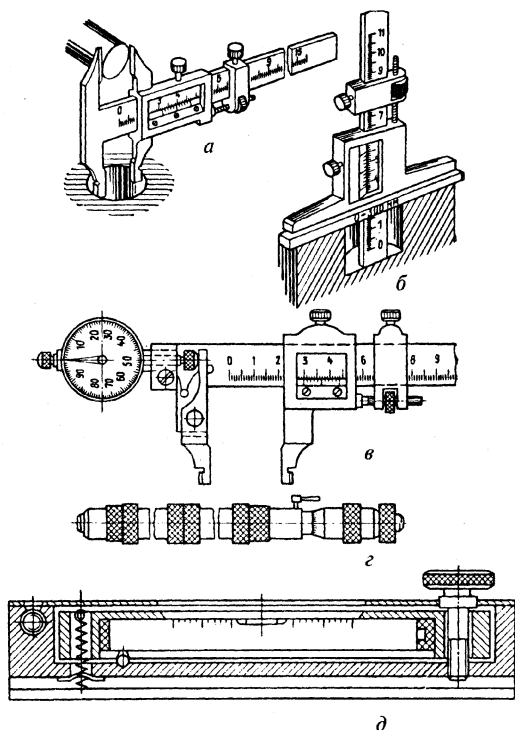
Инструменты для контроля точности сборки и монтажа:
